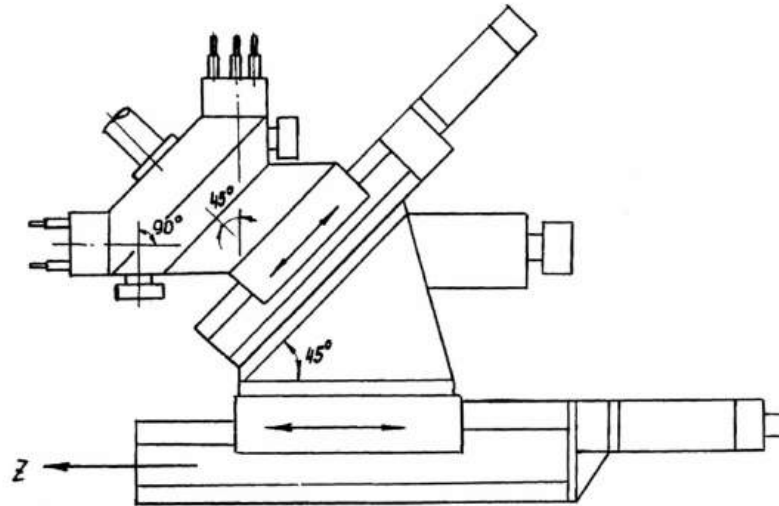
Револьверна головка для багатоінструментної обробки
